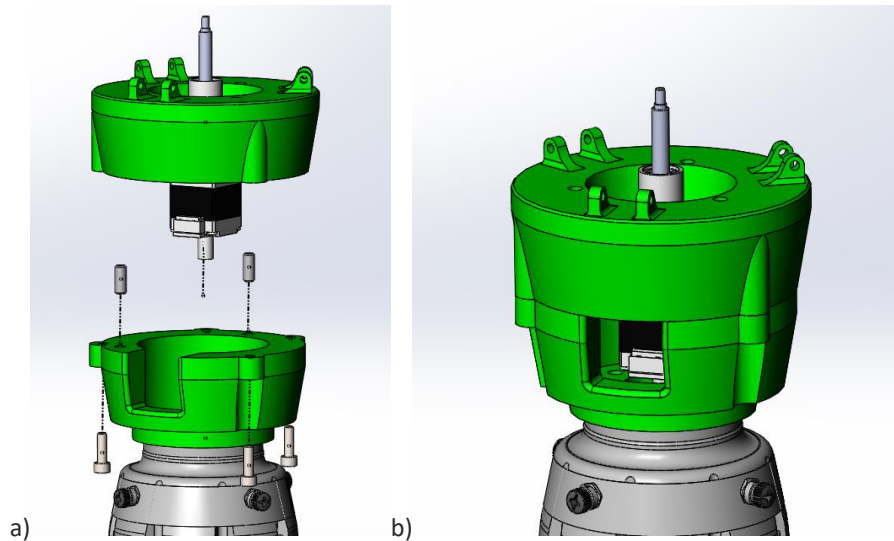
3ª parte da montagem - vista explodida da montagem (a) e parte da montagem completa (b).
